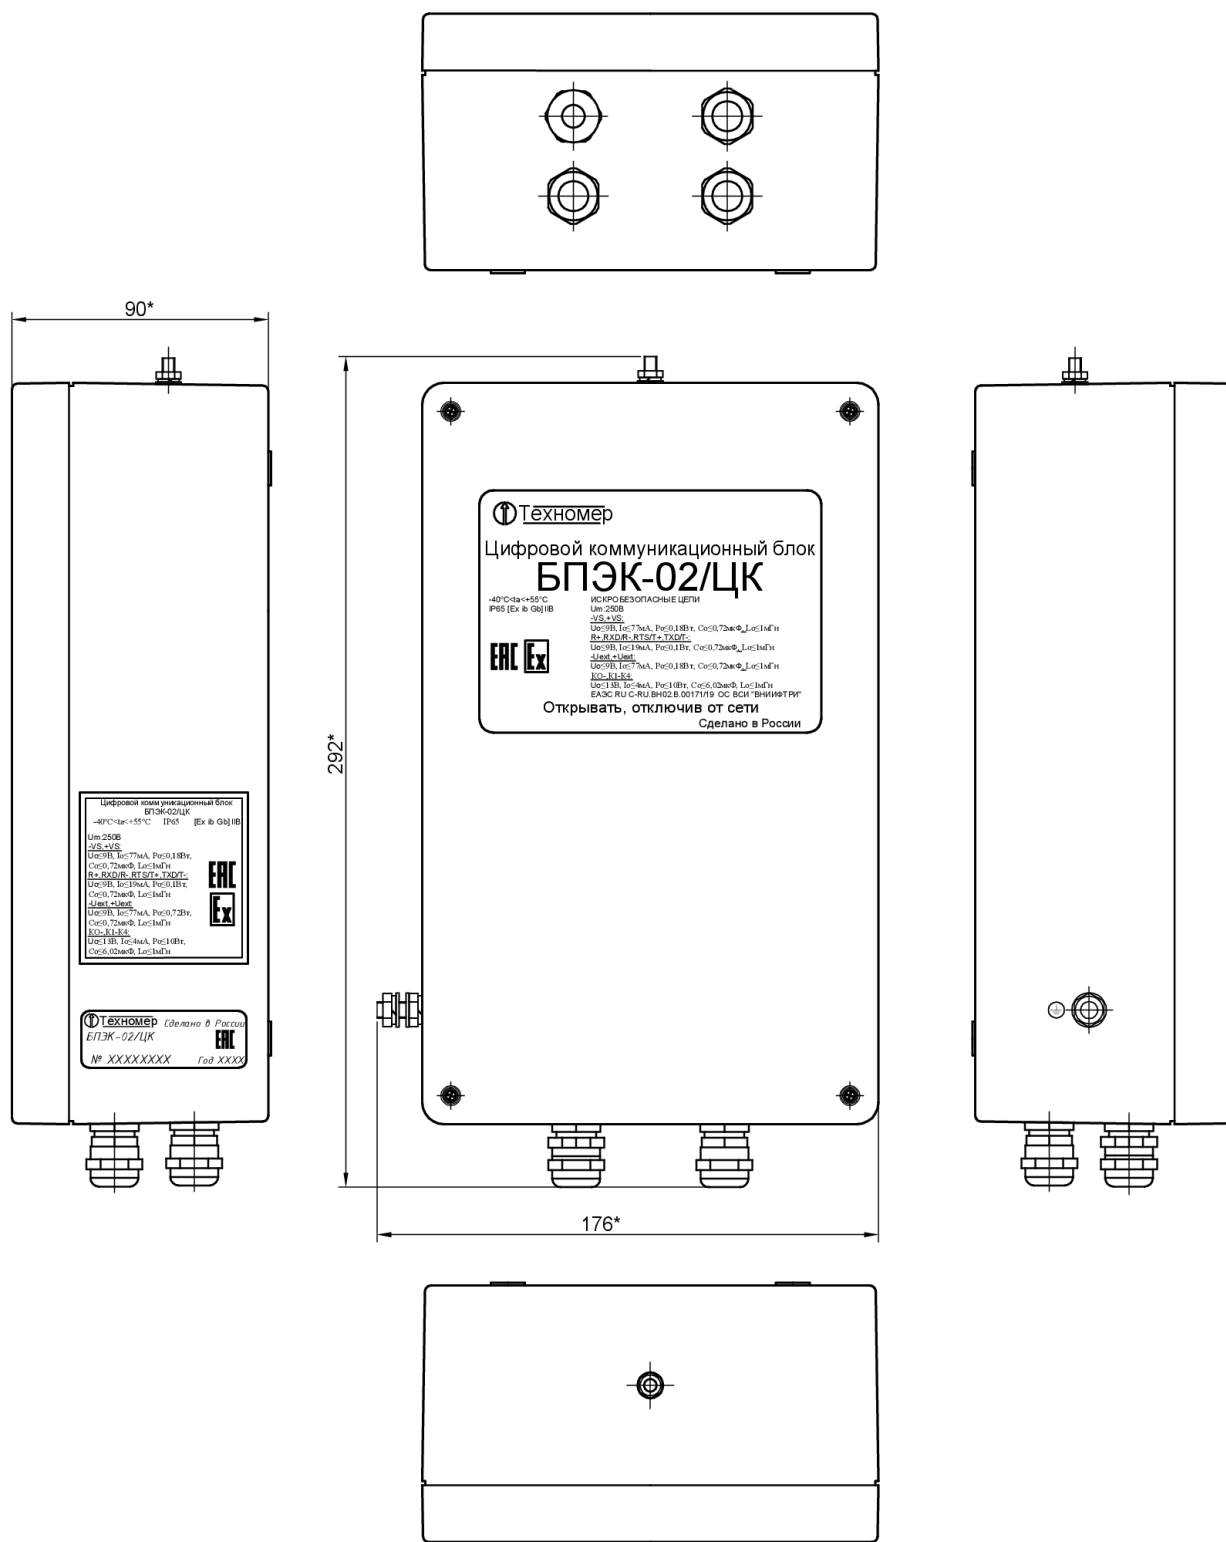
Габаритные размеры блока БПЭК-02/ЦК
